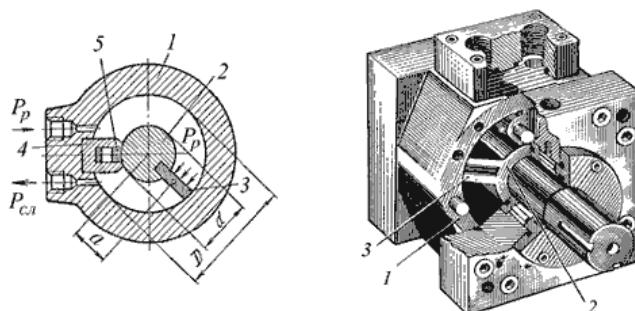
Поворотный однолопастный гидроцилиндр (схема и общий вид)
